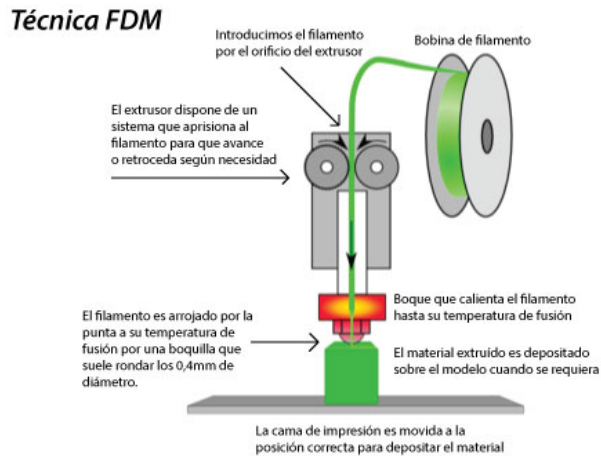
Proceso de impresión. Fuente: comunidad.iebschool.com
